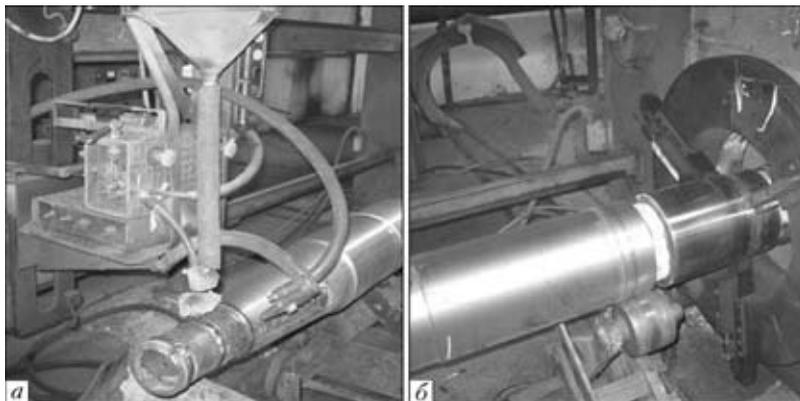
Наплавочная головка установки (а) и установленный в патроне установки
